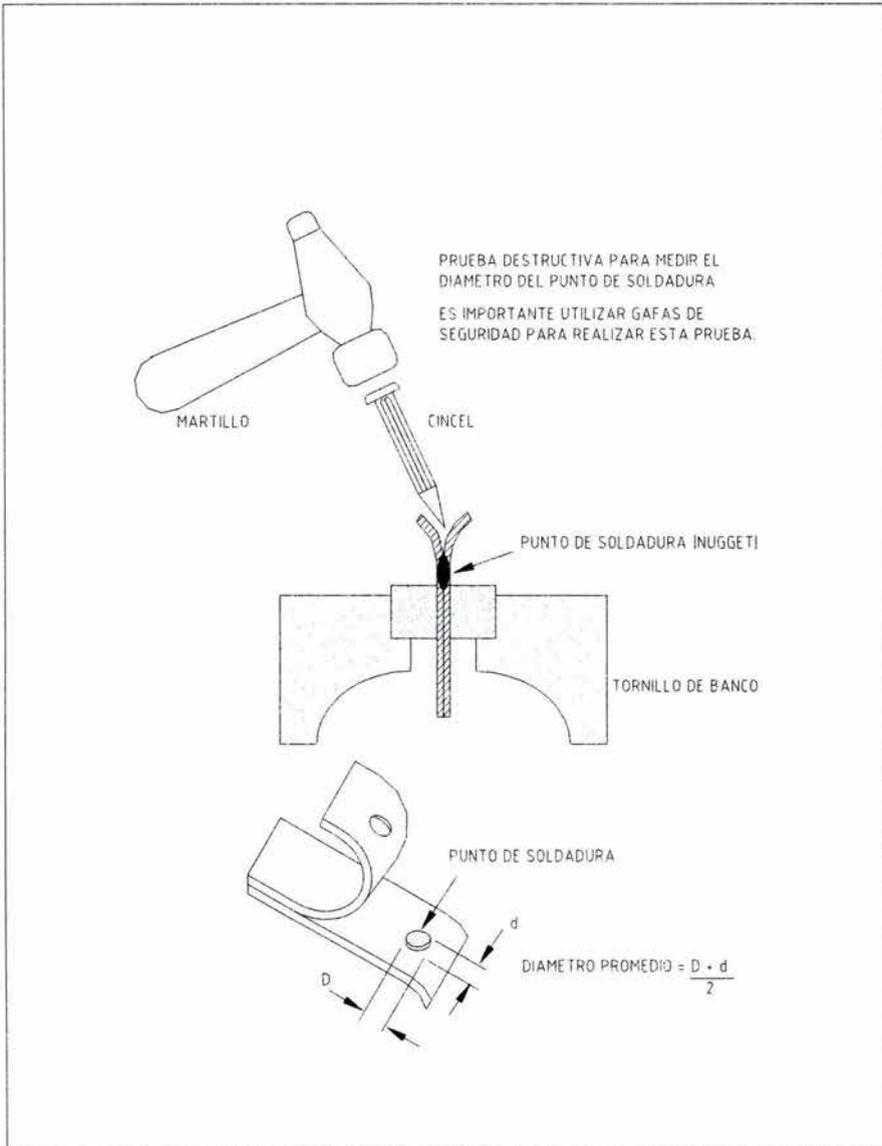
Prueba destructiva para medir el diámetro del punto de soldadura (es importante utilizar gafas de seguridad para realizar esta prueba).
